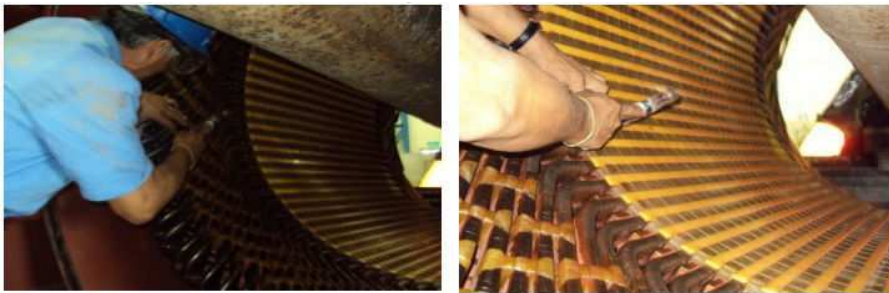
Checagem da amarração das bobinas e fixação das estecas do estator
